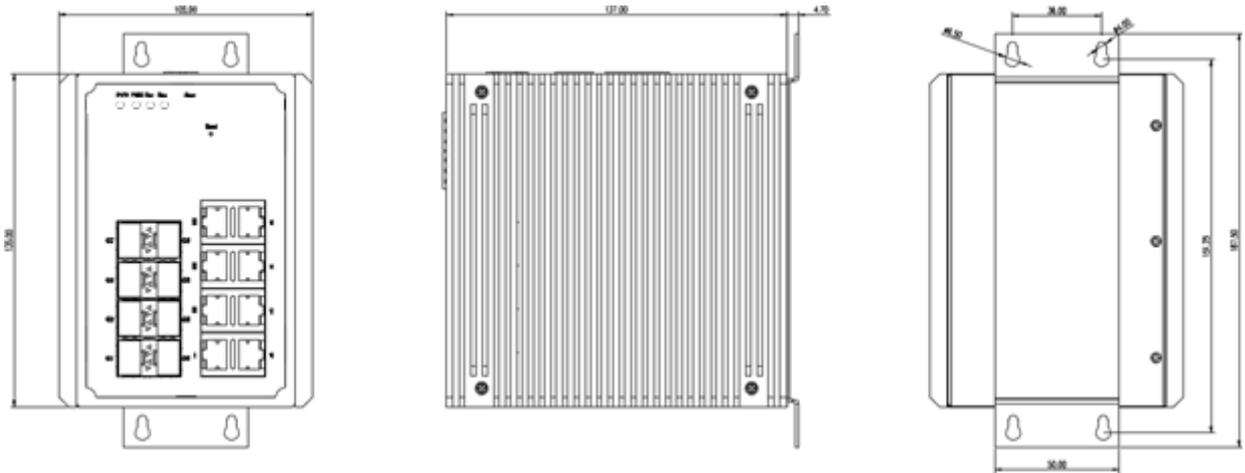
Габаритный чертеж корпуса «Тип 3» с креплением на плоскую поверхность
